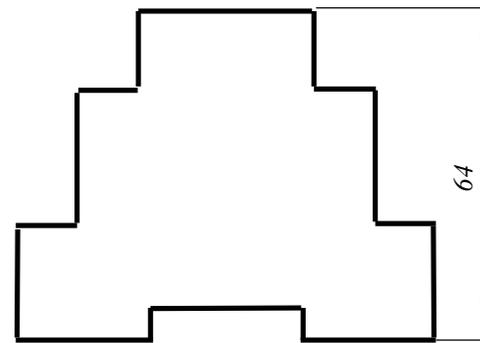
Исполнение в корпусе для крепления на DIN -рейку
